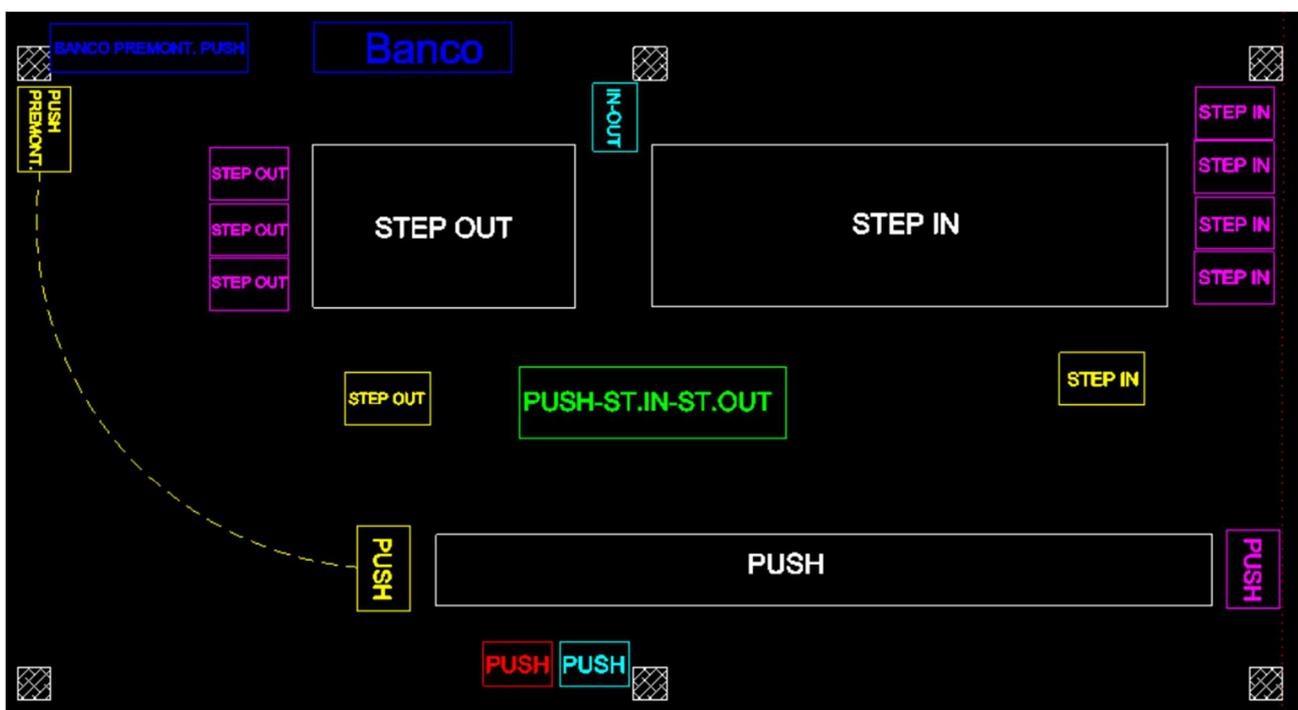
Layout zona di montaggio di Push, Step-in e Step-out, immagine catturata dal Layout elaborato con AutoCAD
